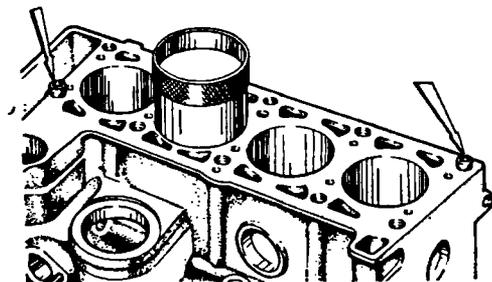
Установка поршня с поршневыми кольцами в цилиндр при помощи монтажной втулки из набора А.60604. Стрелками указаны втулки для центрирования головки на блоке цилиндров
